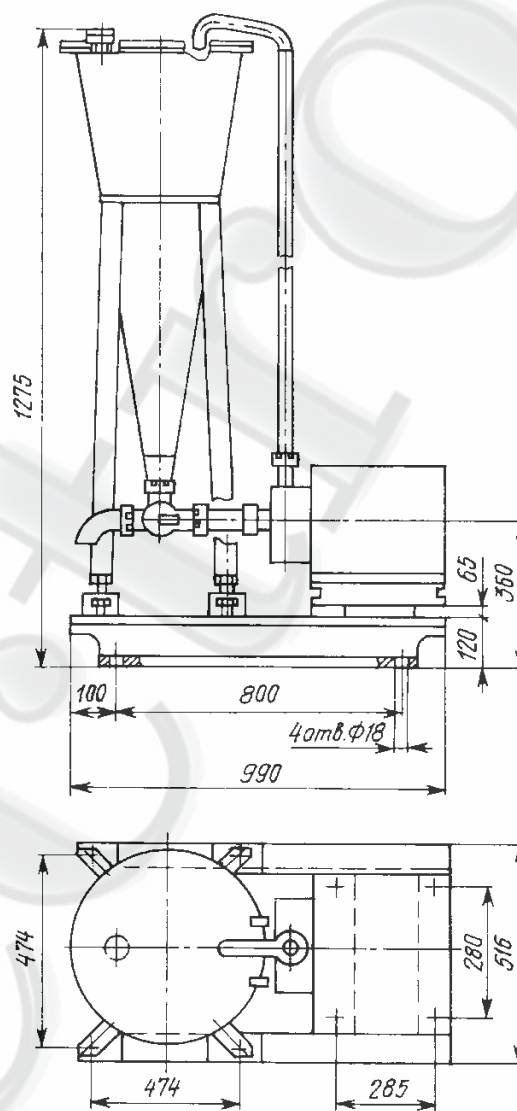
Общий вид, габаритные и установочные размеры РПУ (фермерский вариант)
